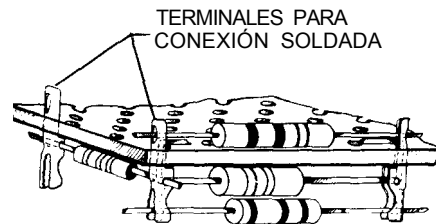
Empleo de terminales insertadas necesarias para conexiones soldadas (Vector Electronic Company Inc.).
